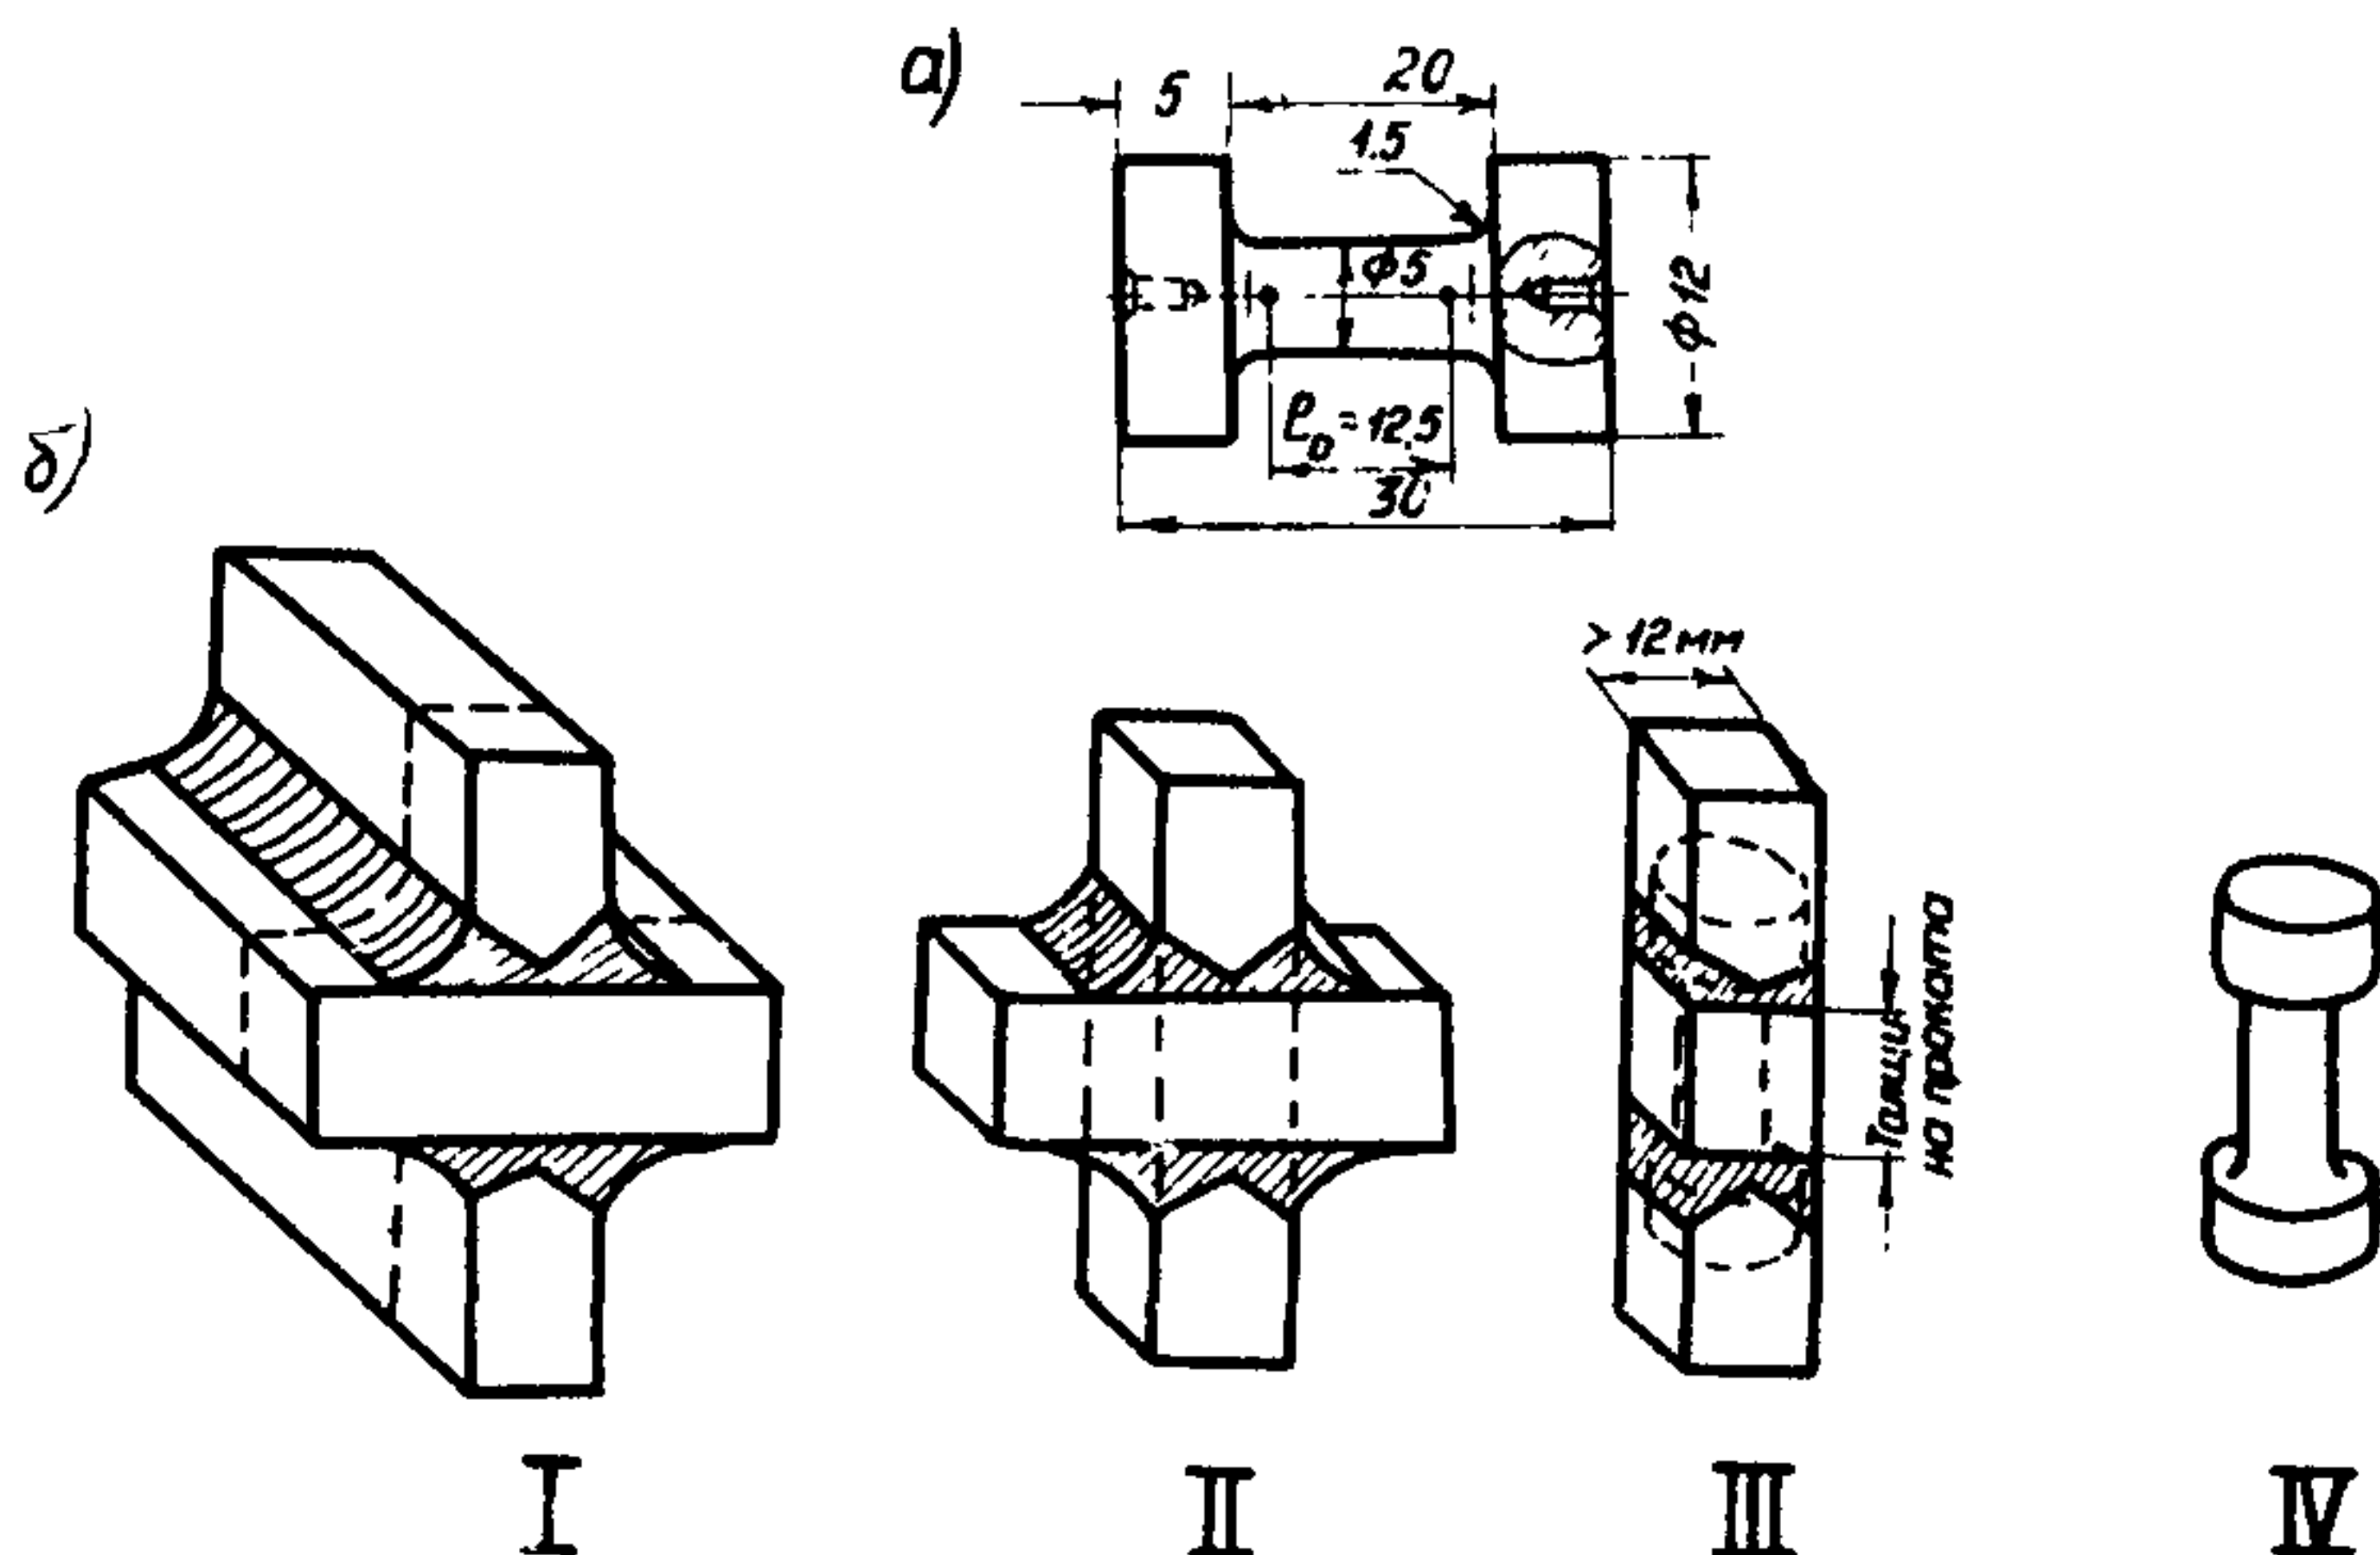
Образец (а) и этапы его изготовления из сварного соединения (б)
